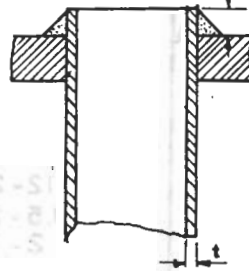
TIPOS DE JUNTAS DE SOLDADURA
